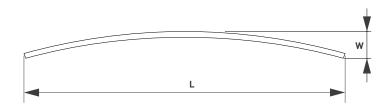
Чертеж и габаритные размеры трека ART-APRIORI-TRACK-ARC-A-1722-5000 (1/10)
